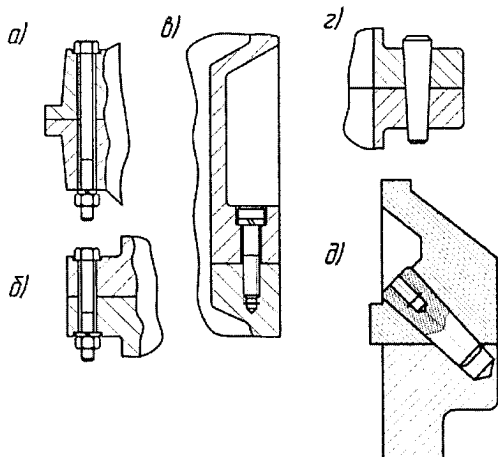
Приклади з'єднань кришки з корпусом редуктора
